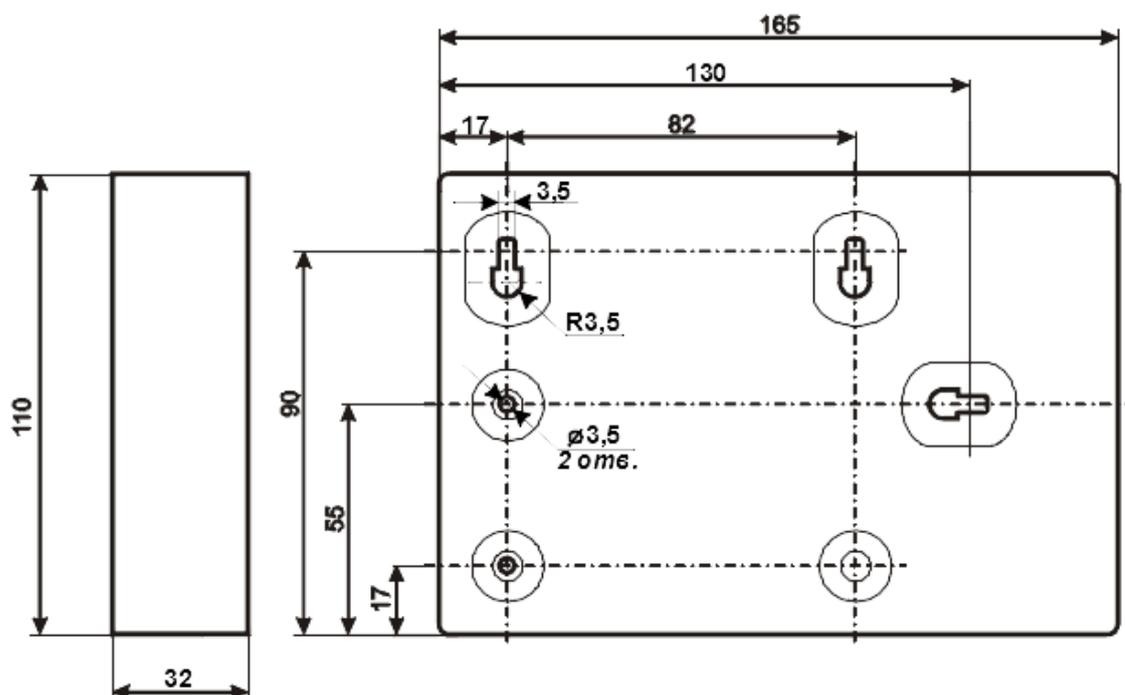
Габаритные и присоединительные размеры КА2, базовый вариант, исп. IP20
